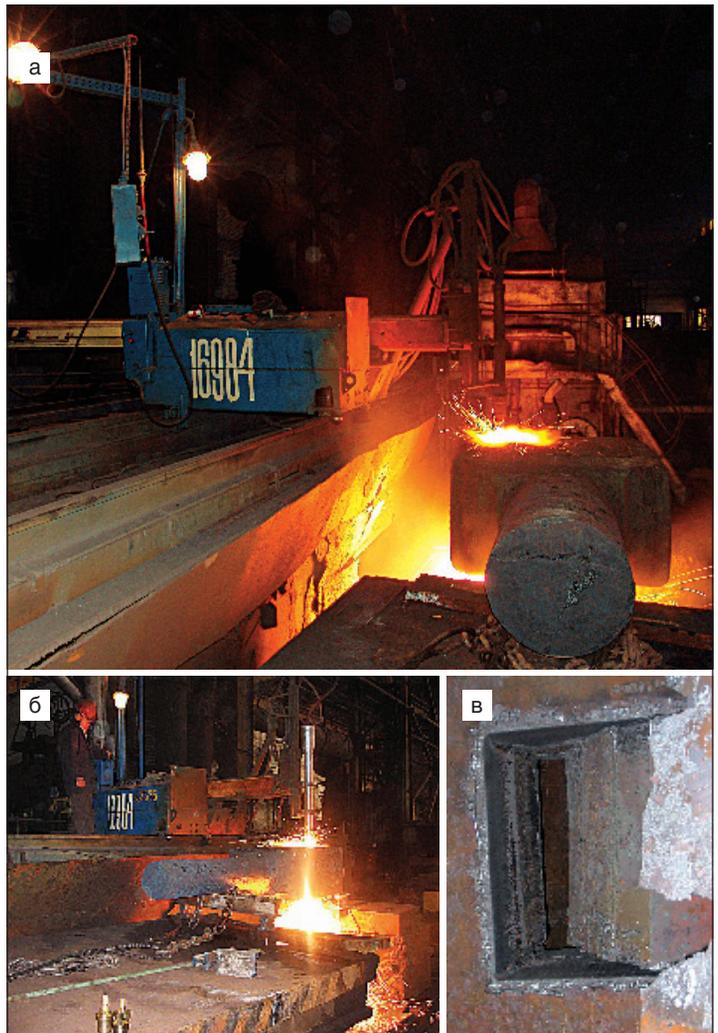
Примеры газокислородной вырезки деталей из плоских поковок: а — коленчатый вал; б — вилка; в — поверхность реза вилки
